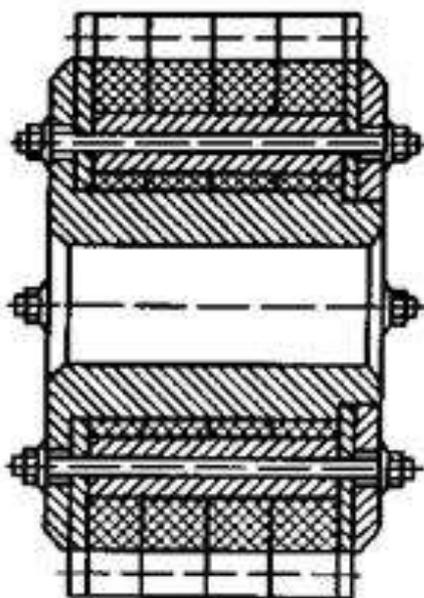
Вариант изготовления неметаллического зубчатого колеса
